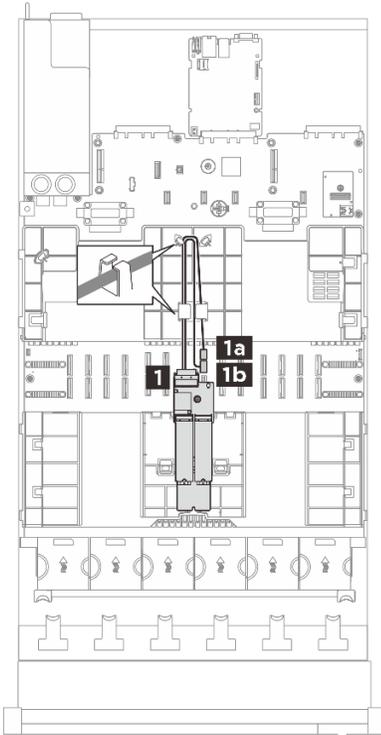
Disposición de los cables para el adaptador de arranque M.2 interno
